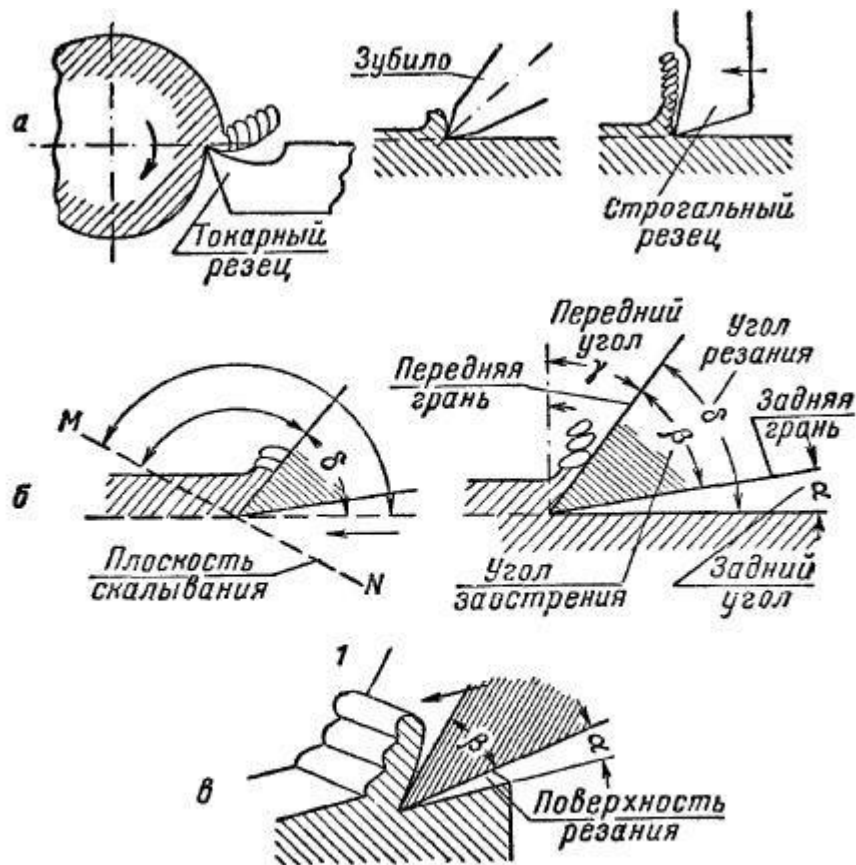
Схема образования стружки и углы режущего инструмента:
